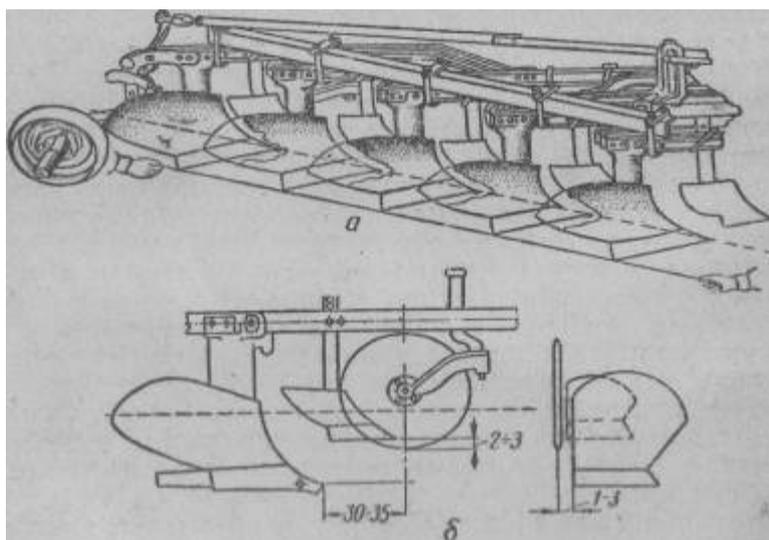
Установка плуга: а -- проверка расположения корпусов; б -- установка продюльжимка- и ножа на раме плуга.
